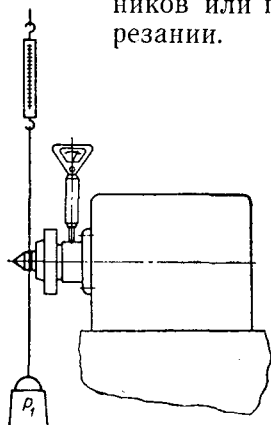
Схема нагружения шпинделя для определения зазора в подшипнике
